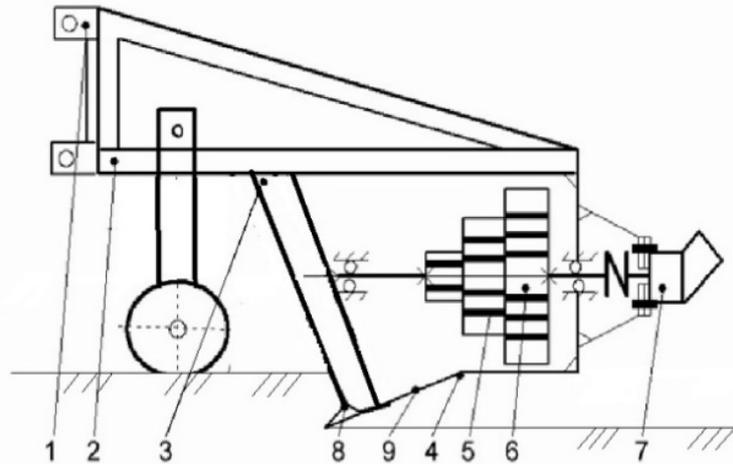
Схема лесопожарной грунтометательной машины: 1 – механизм навески; 2 – рама; 3 – наклонные ножи; 4 – кожух-рыхлитель; 5 – лопатки; 6 – многоступенчатый ротор-метатель; 7 – гидромотор; 8 – скобы с лемехом; 9 – лопатка-подъемник
